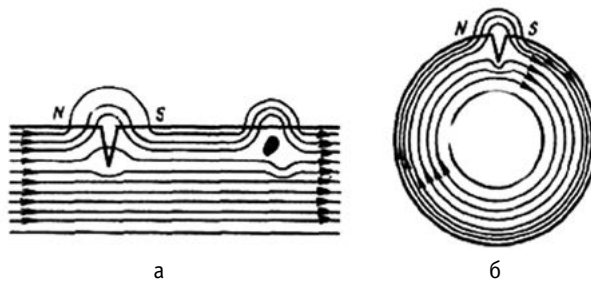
Схеми розподілу магнітних силових ліній за наявності поверхневих і заглиблених дефектів: а – пласка поверхня; б – циліндрична поверхня
